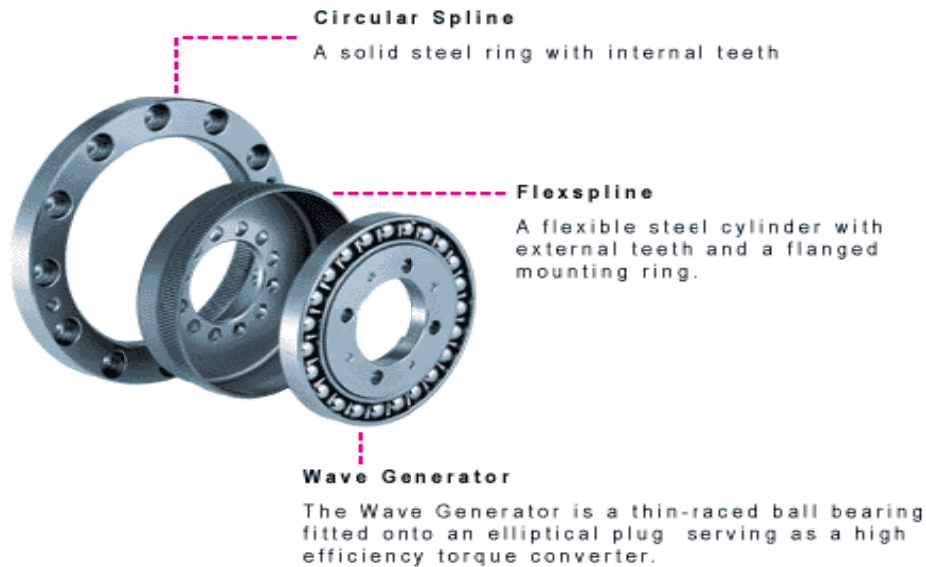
Componentes de un montaje Harmonic Drive AG, CSD.
